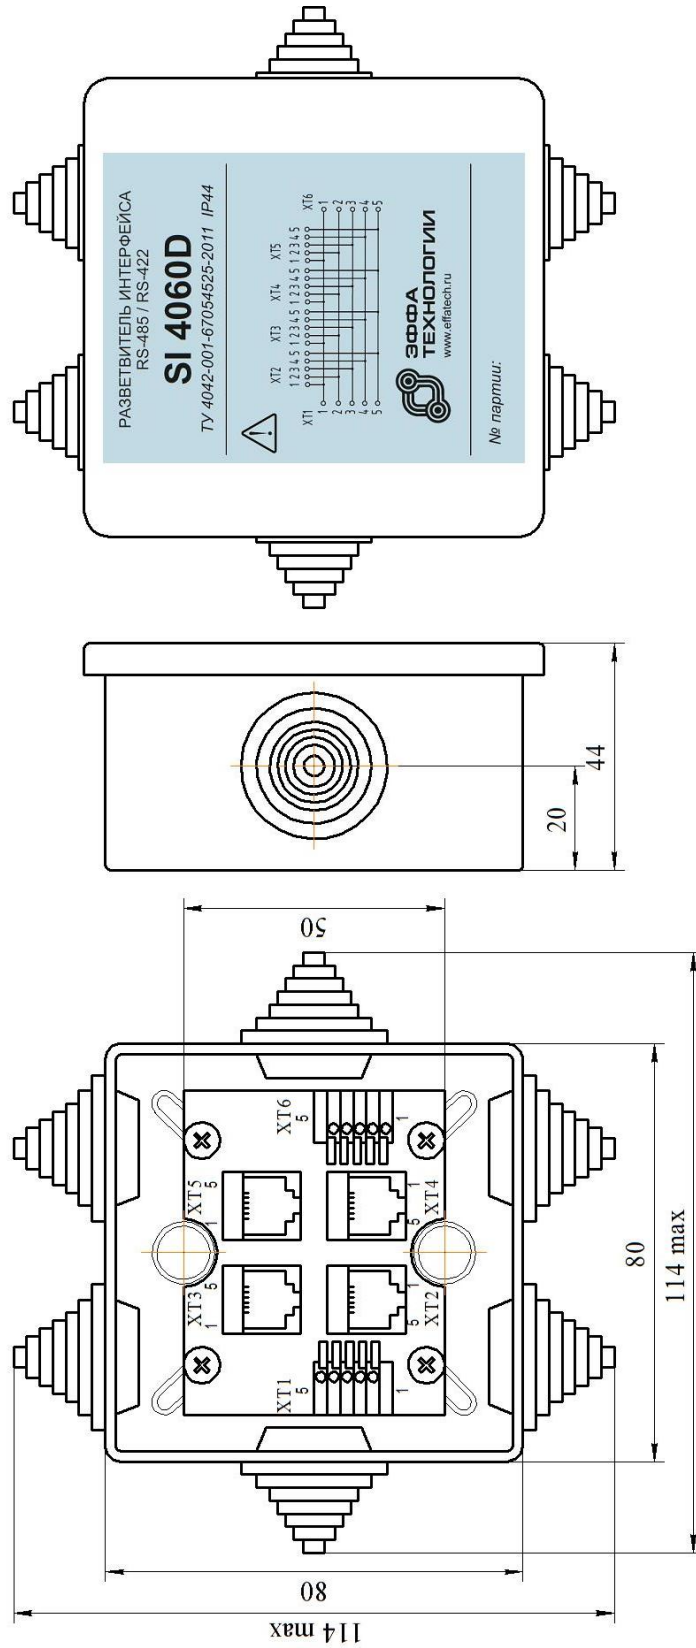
Габаритные и установочные размеры разветвителя SI 4060D
